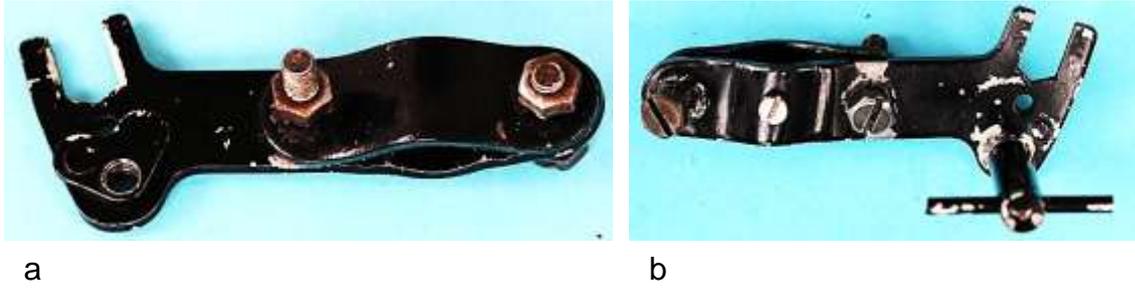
Halter mit Klemmschuh: a) Halter mit Verstärkungsblech und Befestigungsschelle, b) Halter mit Masseschraube und eingedrehter Knebelschraube
